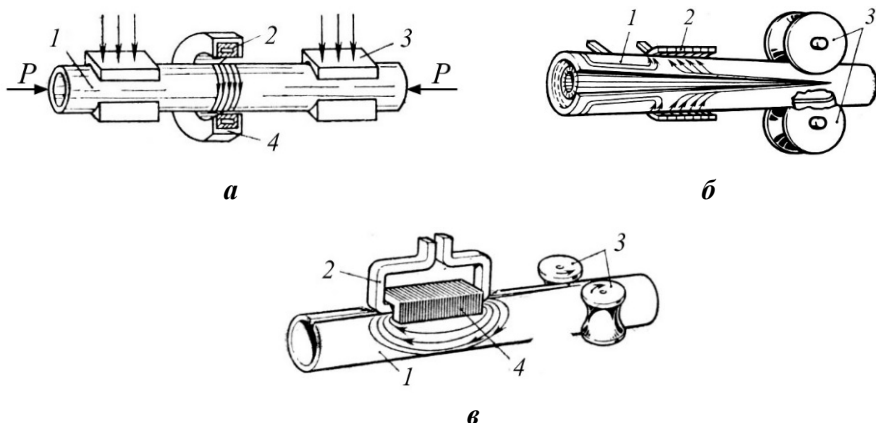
Схеми високочастотного зварювання труб з індукційним нагріванням:
